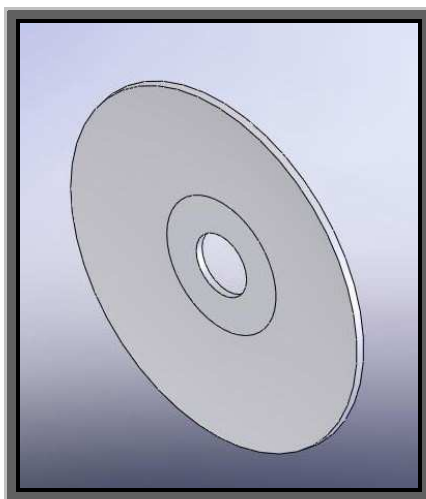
Vista isométrica y frontal de la rueda del conjunto rueda giratoria.
